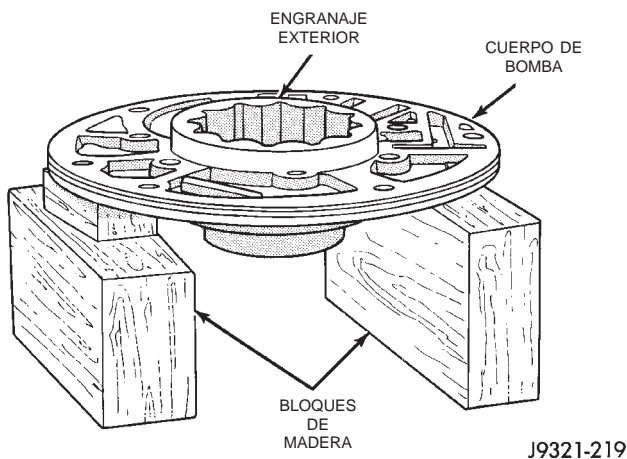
Apoyo de la bomba e instalación del engranaje exterior
